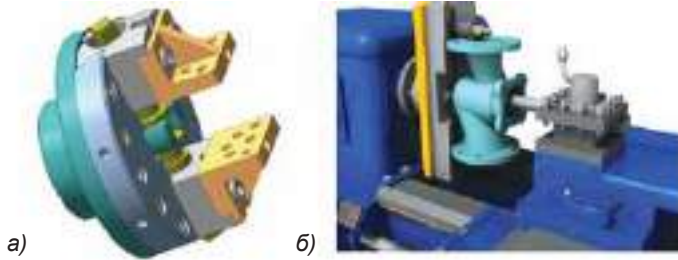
Двокулачкові патрони: а — загальний вигляд; б — встановлення деталі складної форми у двокулачковому патроні
